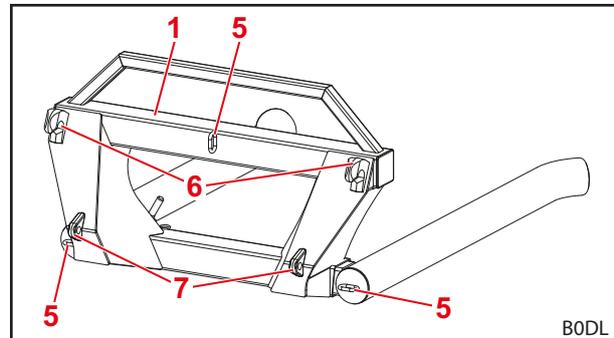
Estructura del aparato de transporte de pacas H – Vista posterior
